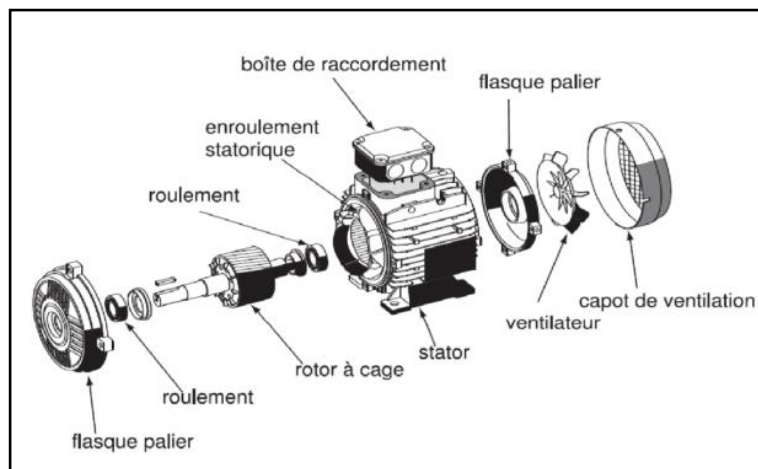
Vue détaillé d'une machine asynchrone à cage d'écureuil. [14]
